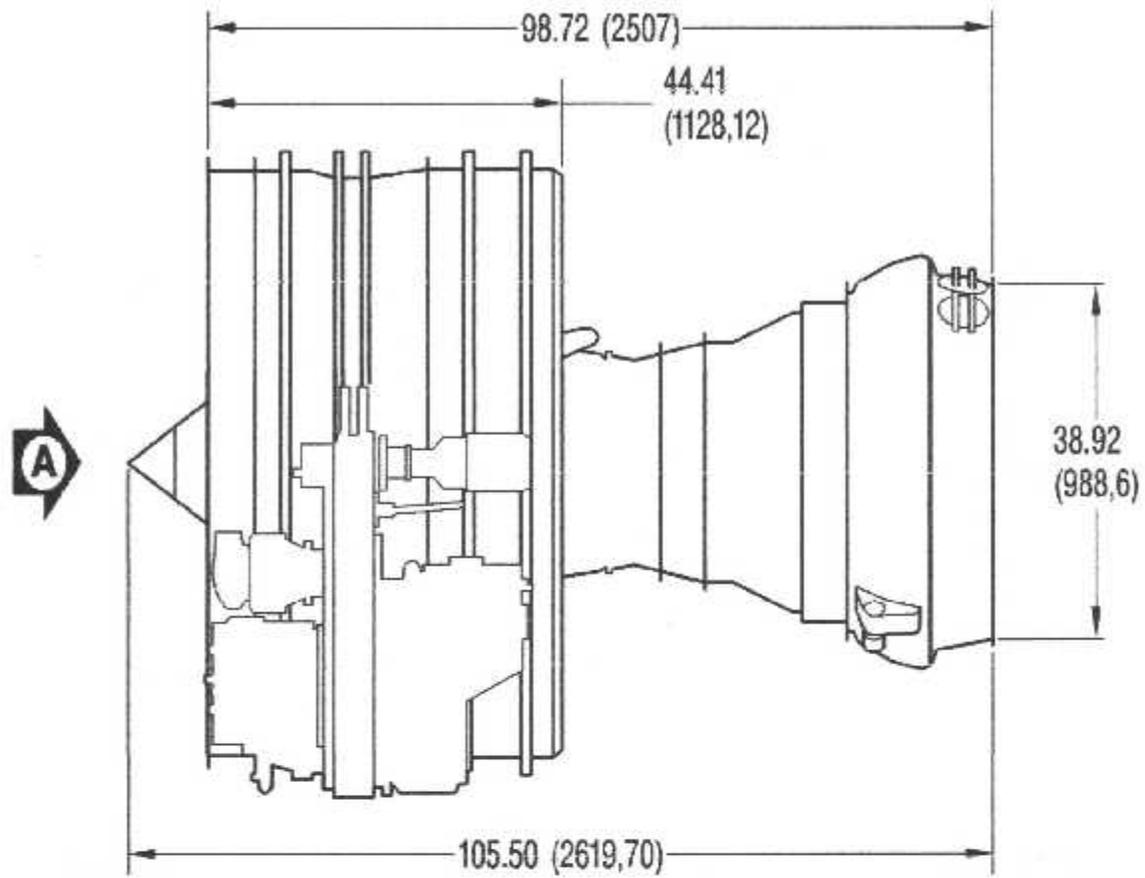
Vue Arrière du Moteur CFM56-7B.
